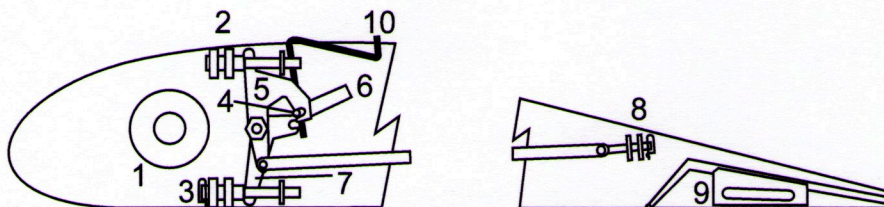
Holmanschluss mit Bolzen in gesichertem Zustand
